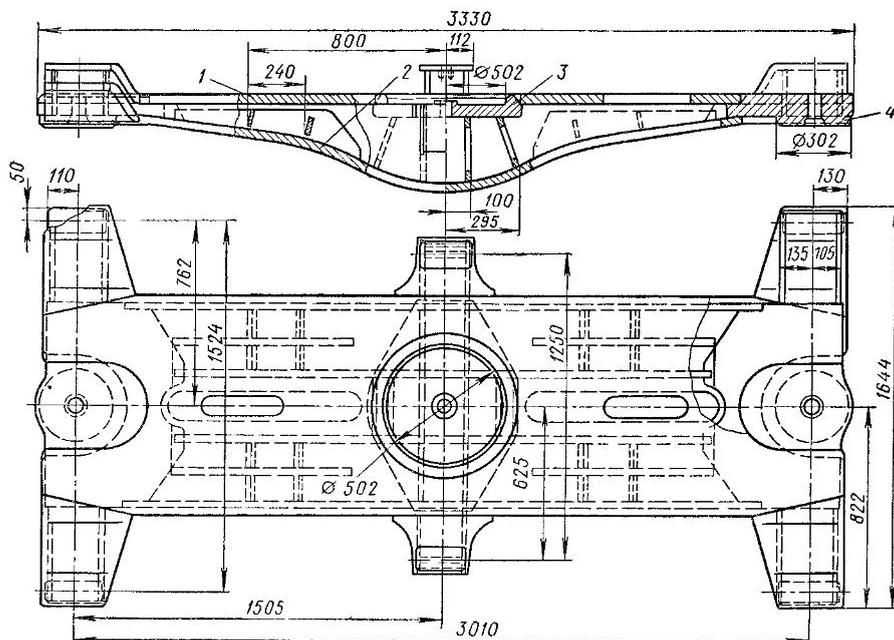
Штампосварная соединительная балка четырехосных тележек вагонов-самосвалов
